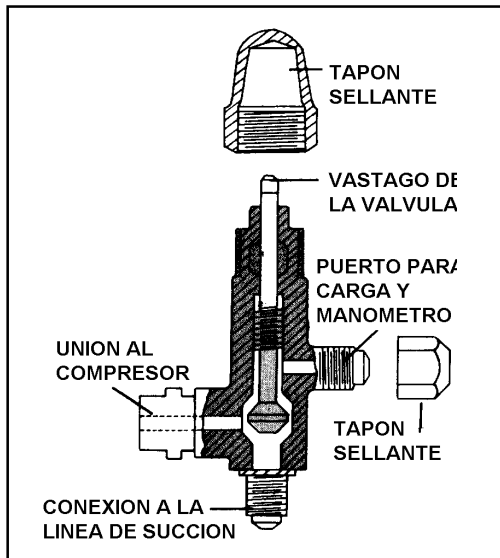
Válvula de servicio para compresor hermético, soldable.
